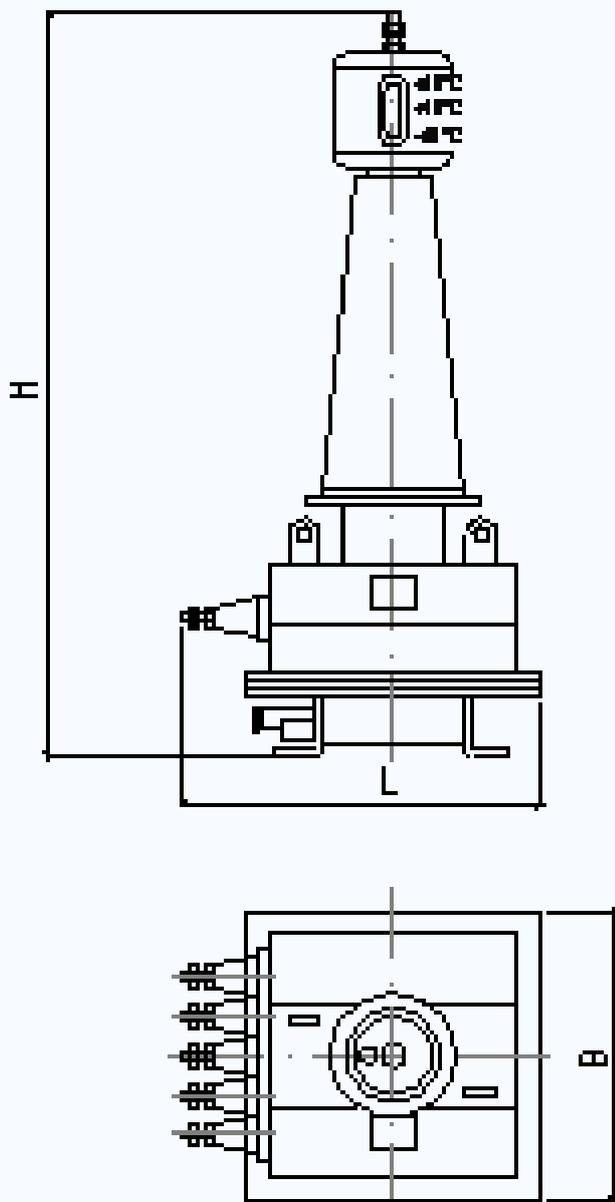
Общий вид и габаритные размеры трансформаторов типа ЗНОМ-35-Б-У1
